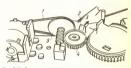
Снятие двигателя привода томарма: I — пассик; 2 — стопор; 3 — нажать стопор в направлении, увязанном стрелкой; 4 — промежуточное зубчатое колесо; 5 — червях
